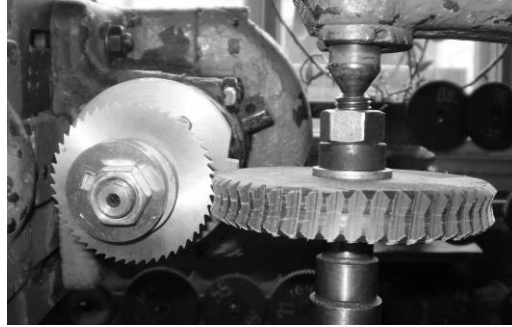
Нарізання глобоїдного черв'ячного колеса дисковою фрезою на зубофрезерному верстаті
